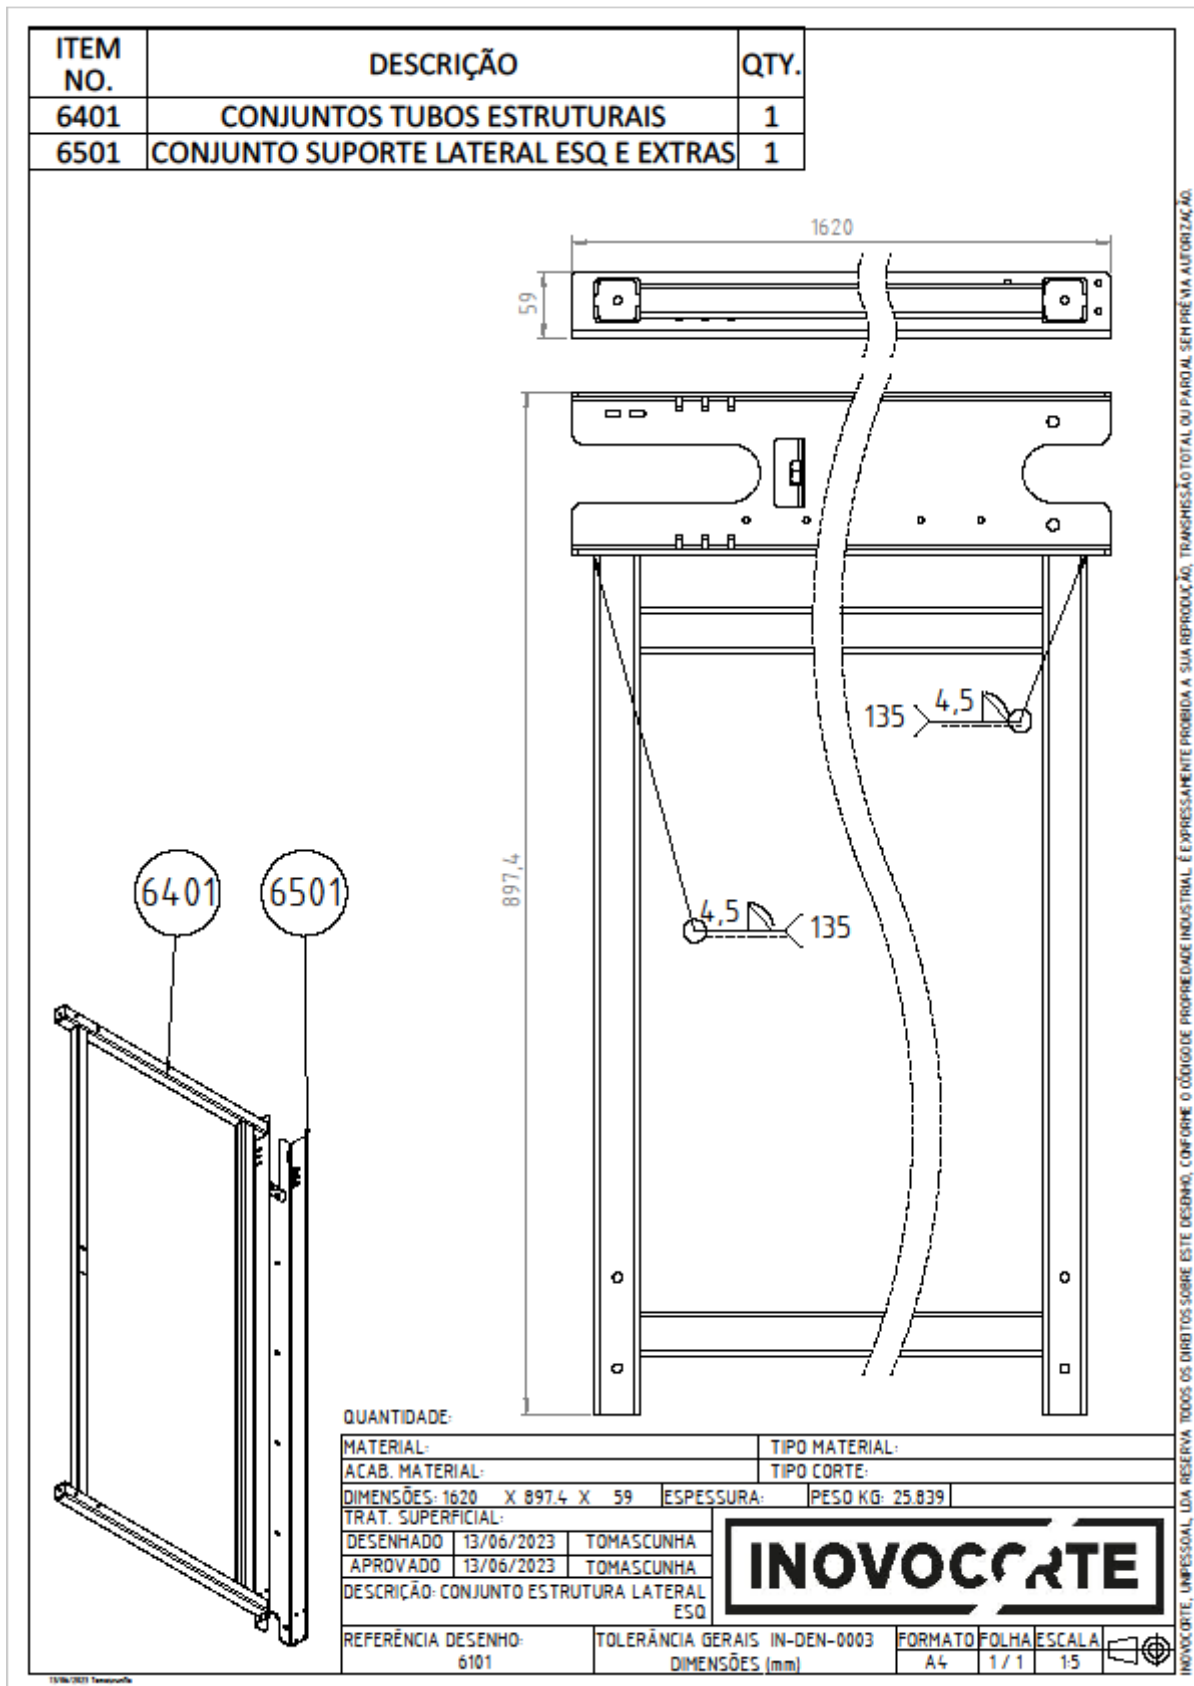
Desenho técnico do conjunto estrutura lateral esquerda (6101).
